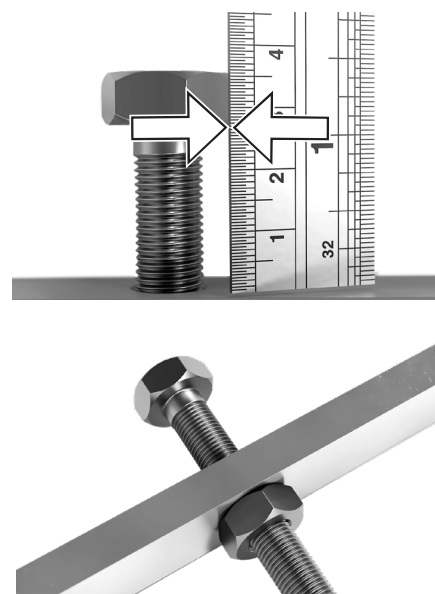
B - Régler le boulon à la hauteur de coupe voulue et serrer l'écrou (réglage à 27 mm pour l'exemple ci-dessus).
